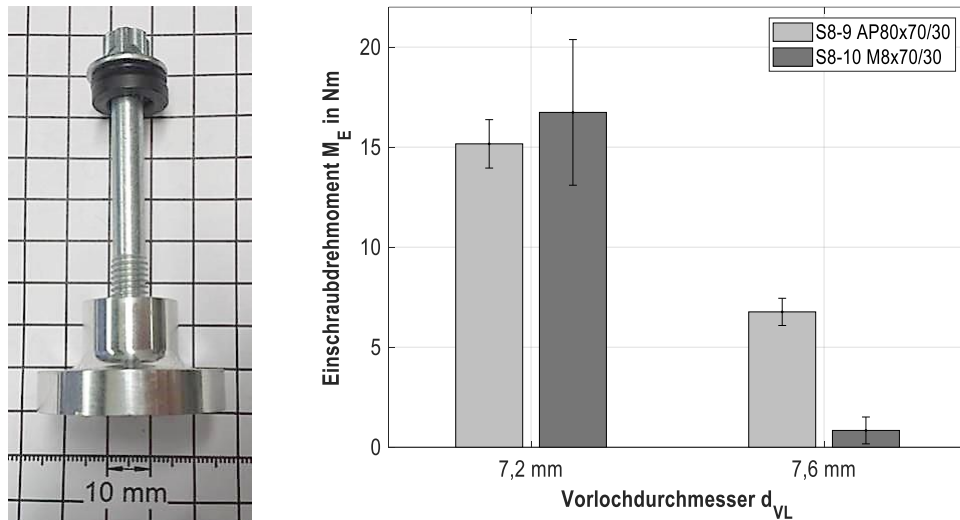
Schraube montiert in Mutternkörper (links), ermitteltes Einschraubdrehmoment für zwei ausgewählte Vorlochdurchmesser $d_{VL} = 7,2$ mm und $d_{VL} = 7,6$ mm (rechts)
